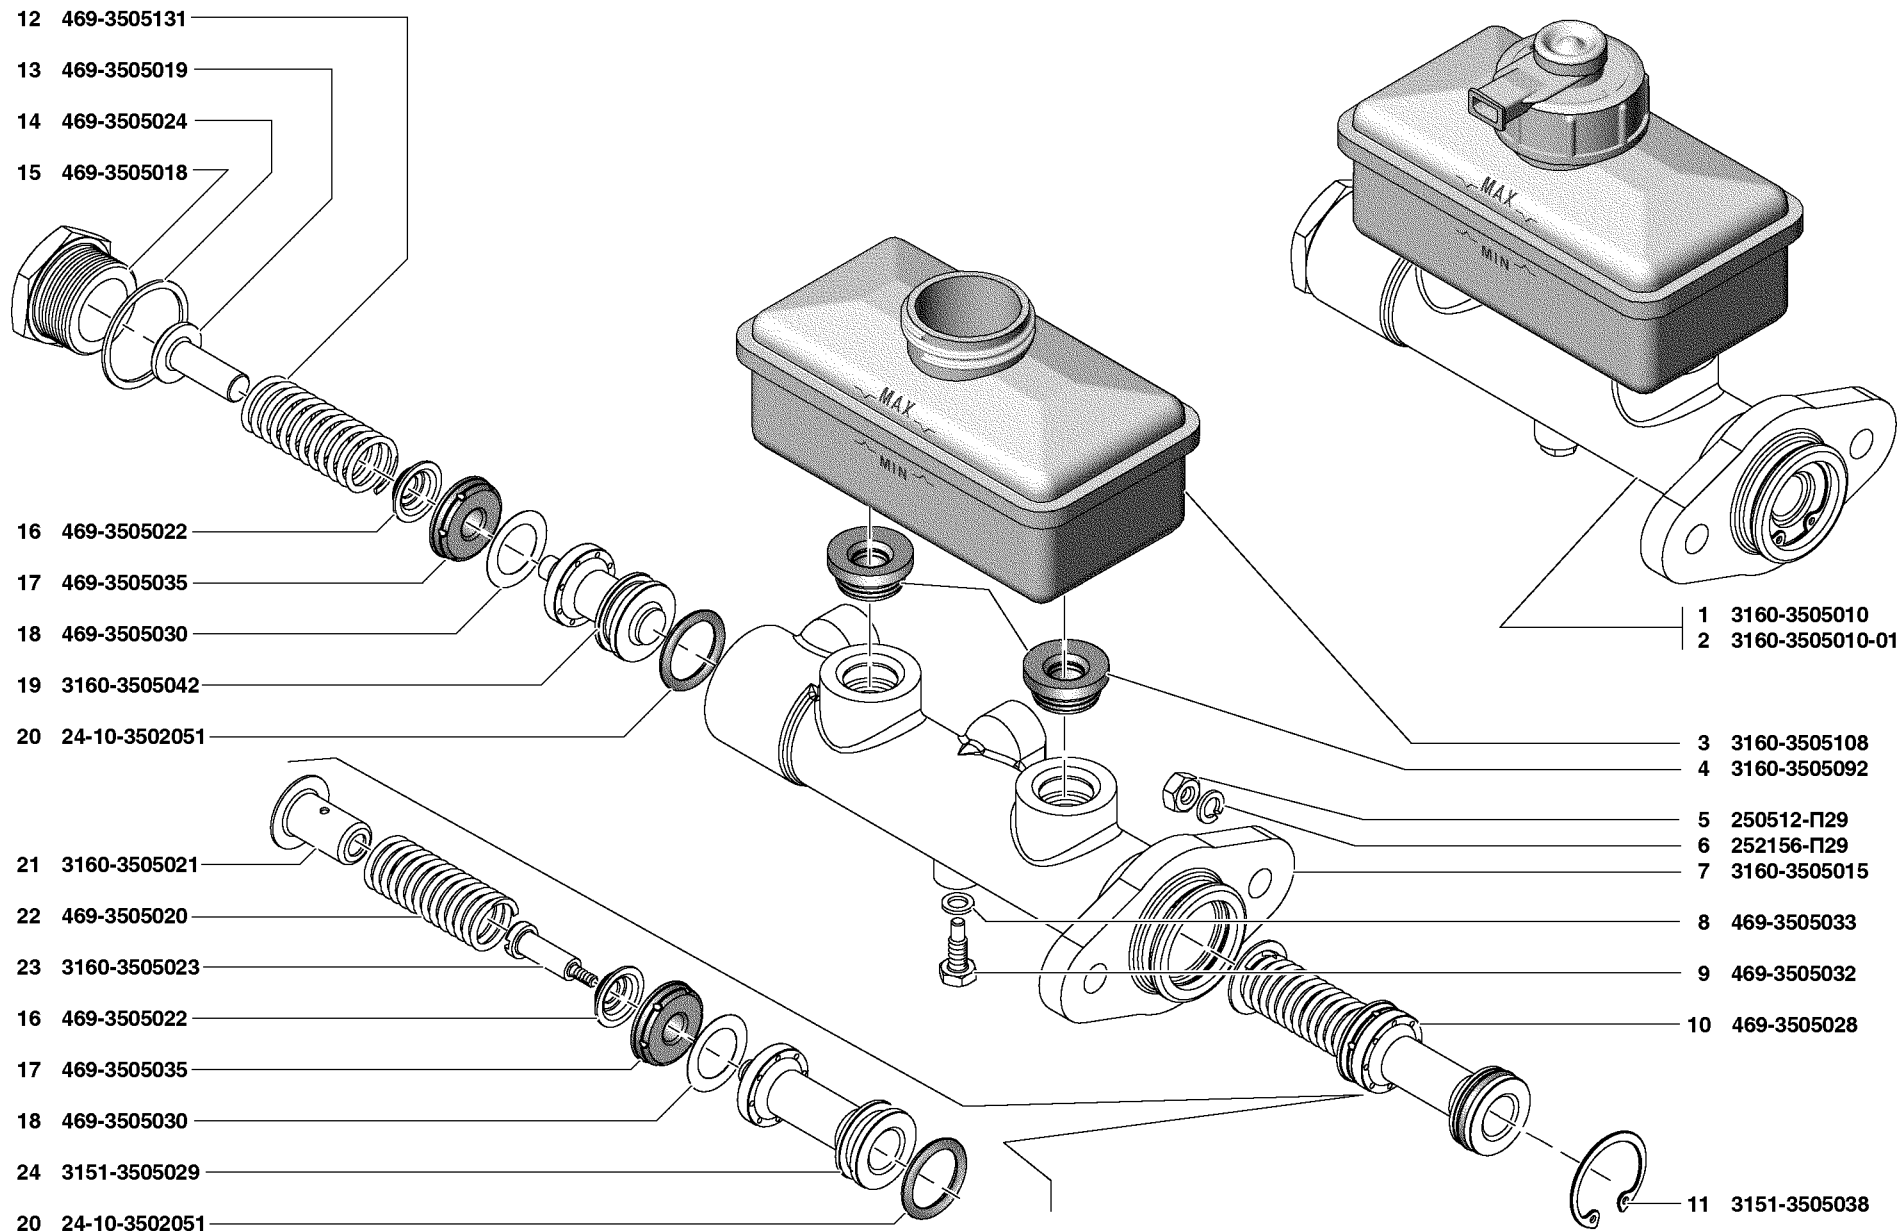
Цилиндр главный гидравлических тормозов (3505)
